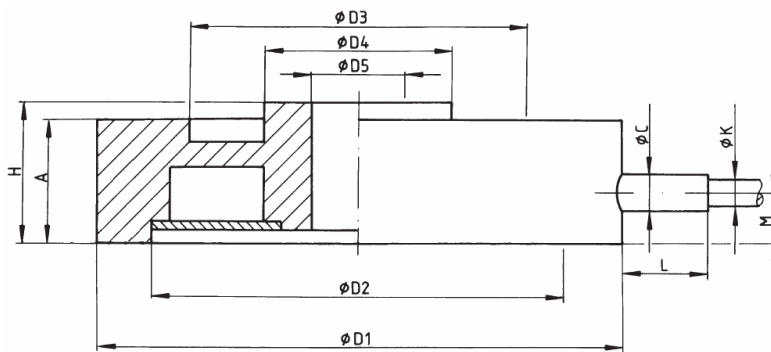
Disegno tecnico e dimensioni delle celle di carico
